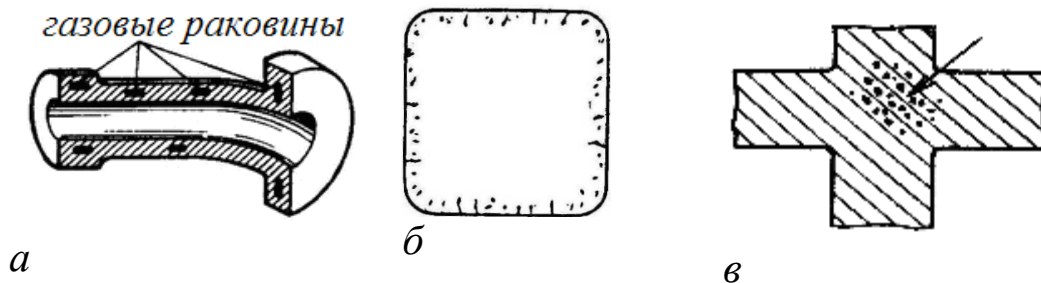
Газовые раковины в отливках: а – в теле отливки; б – вблизи поверхности (подкорковые пузыри); в – усадочная пористость
